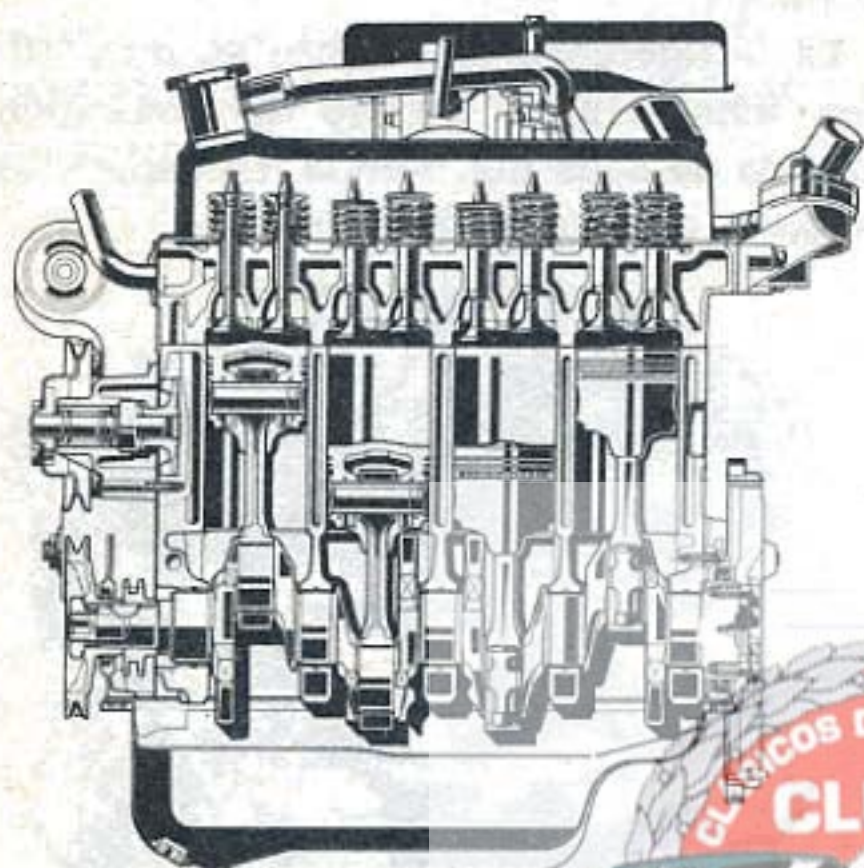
Corte longitudinal del motor, de válvulas en cabeza y cigüeñal de cinco puntos de apoyo.
